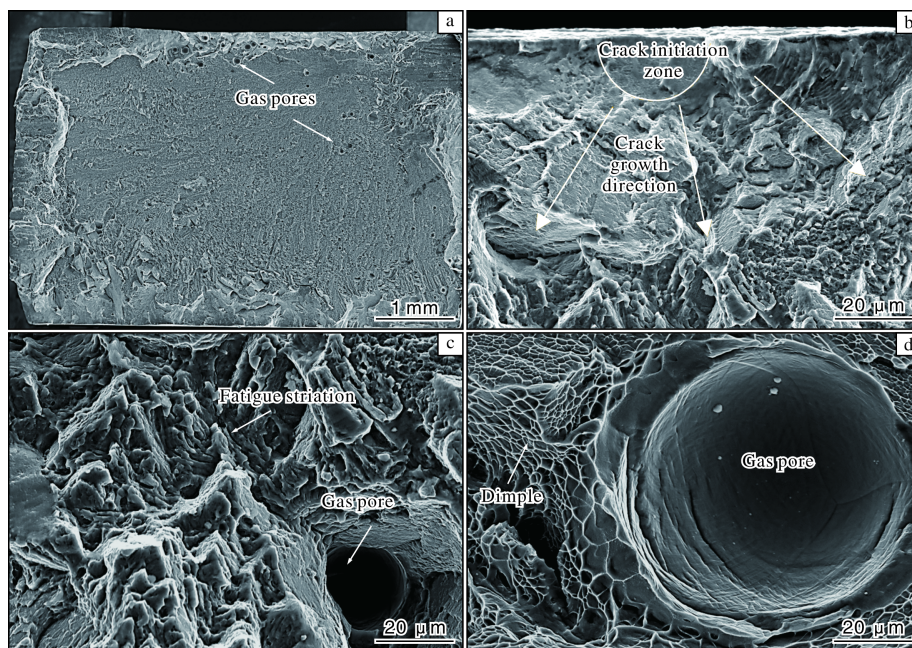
TC17/Ti60 合金激光焊接接头的低周疲劳断口形貌
